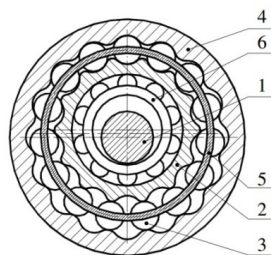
Схема передачи с ПТК и свободной обоймой: 1) генератор; 2) кулачок; 3) ролики; 4) венец; 5) обойма-сепаратор; 6) подшипник
